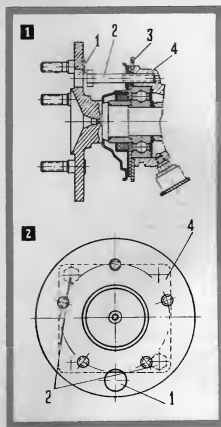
Так выпрессовывается полуось: 1 — технологическое отверстие; 2 — болты М10 длиной 70 мм; 3 — опорный диск; 4 — фланец кожуха.
